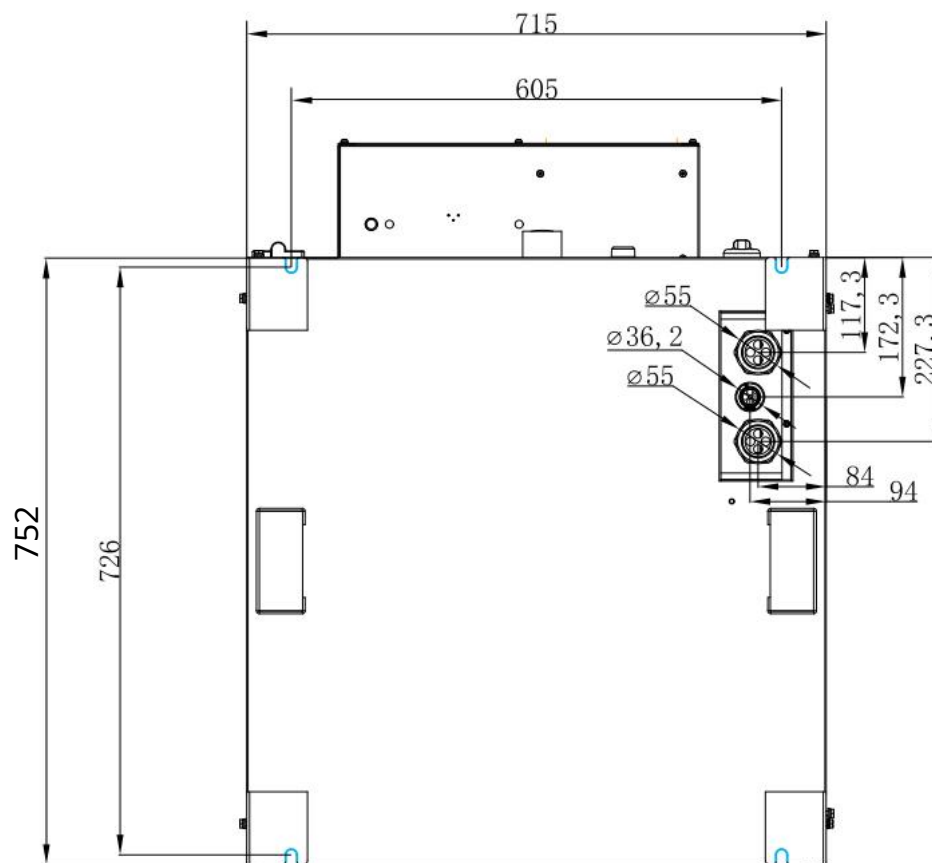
Ubicación de las ranuras de montaje debajo del gabinete
